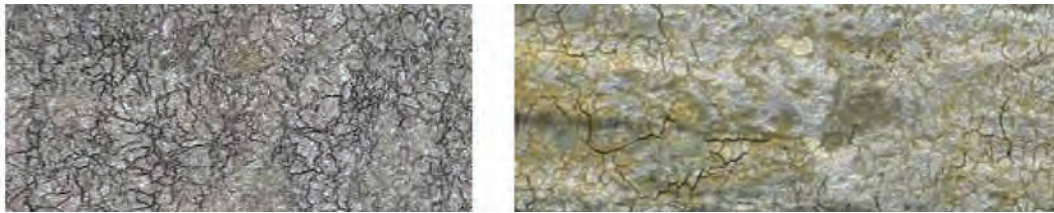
Сетчатые трещины на поверхности непрерывной заготовки сечением 300×400 мм
